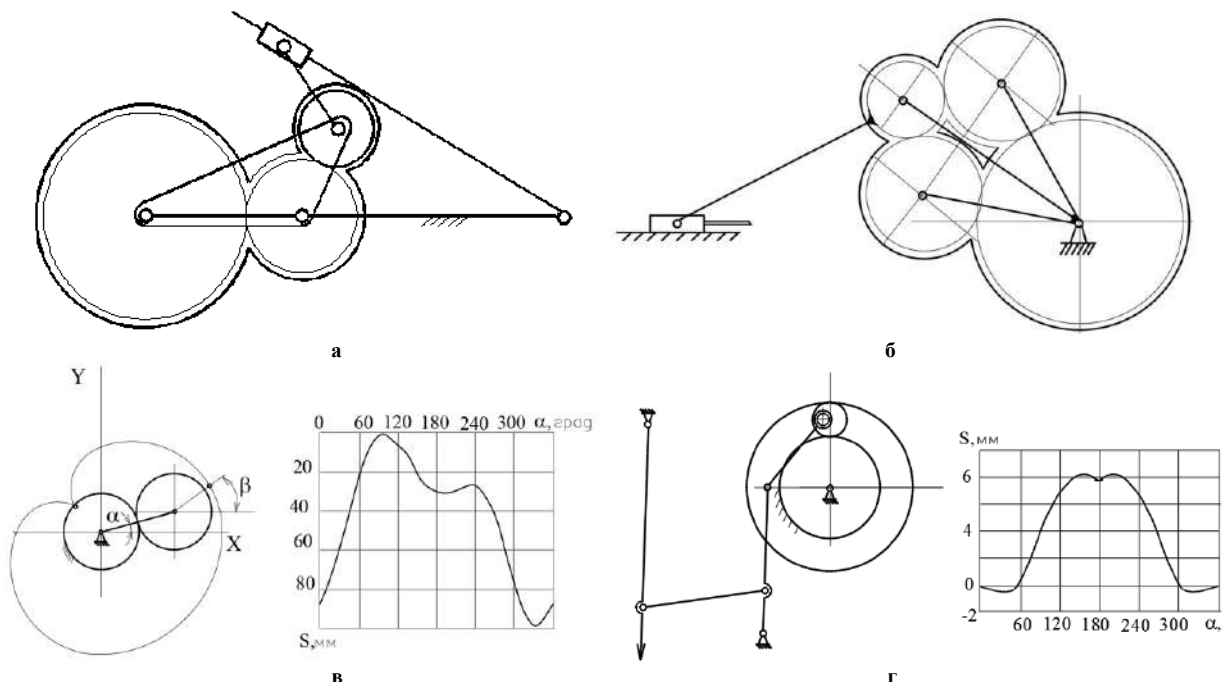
Зубчато-важільні механізми: а - механізм з коливальним рухом вихідної ланки; б - механізм приводу рапір ткацького станка типу АТПР; в - планетарний механізм ниткопритягувача швейної машини; г - планетарний механізм відхилення рамки швейної машини
